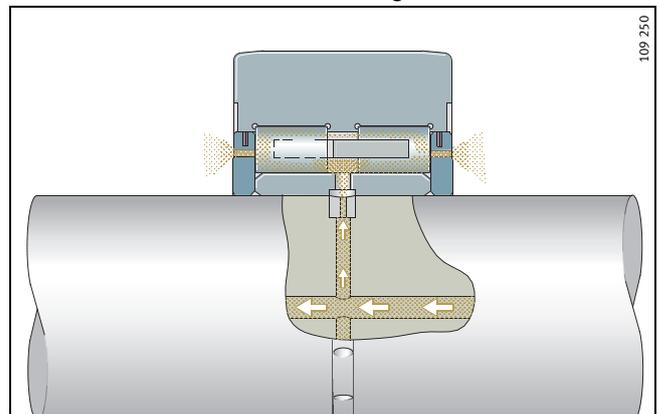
· Minimalmengen-Schmierung – Stützrolle mit Lamellenring
